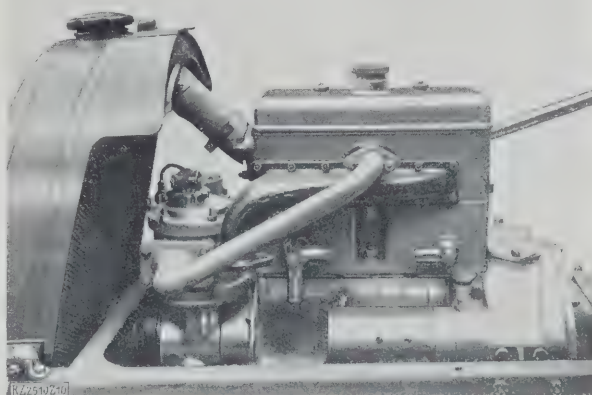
1,5 l-B.N.C.-Viertaktmotor mit Cozette-Kompressor
